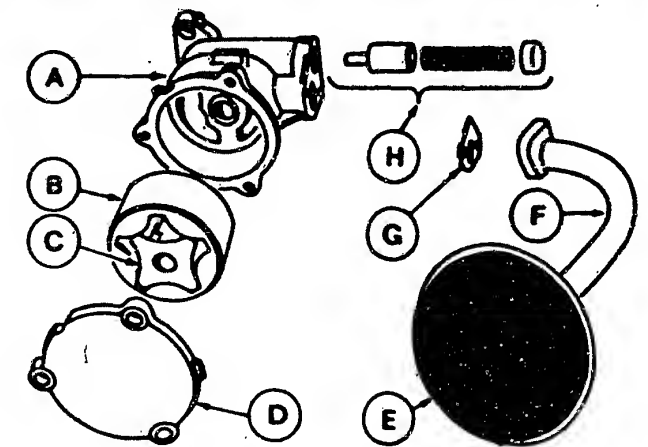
Einzelteile der Ölpumpe des OHC-Motors: A Gehäuse – B Äusserer Rotor – C Innerer Rotor – D Deckel – E Ölsaugsieb – F Saugrohr – G Dichtung – H Überdruckventil.
